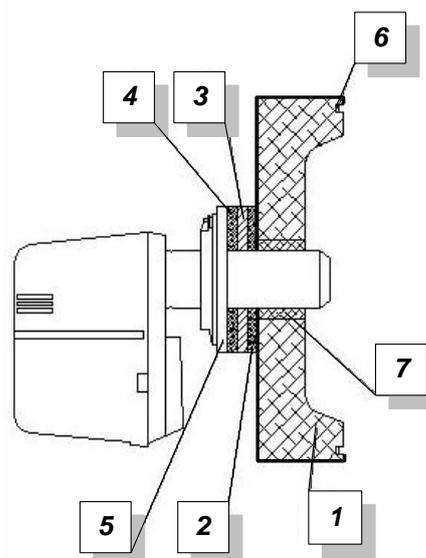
Схема установки горелки на дверку котла КОЛВИ
